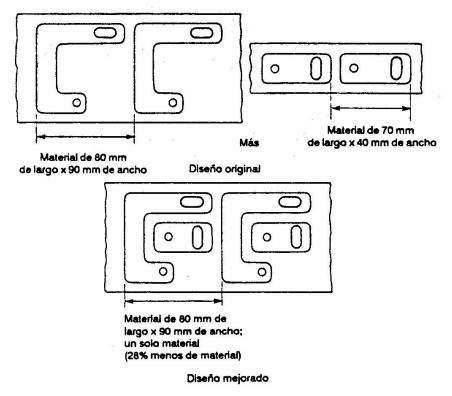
Los rediseños pequeños permiten que una pieza pueda cortarse del material sobrante del recorte de otra pieza.
